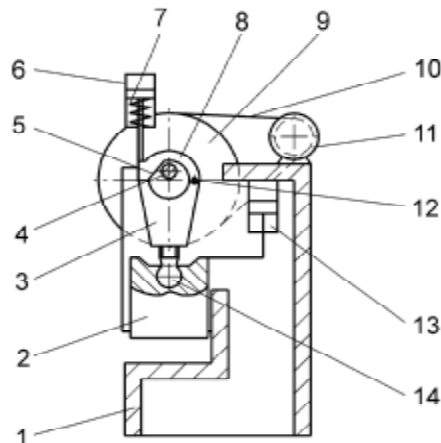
Загальний вигляд механічного безмуфтового преса з поворотною кришкою шатуна
